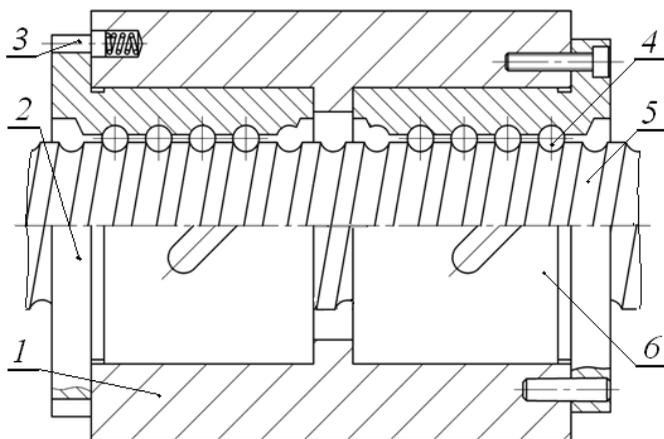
Передача винт-гайка качения с поворотом одной гайки 2 в корпусе 1 относительно винта 5 для регулирования натяга при фиксированной второй гайке 6
